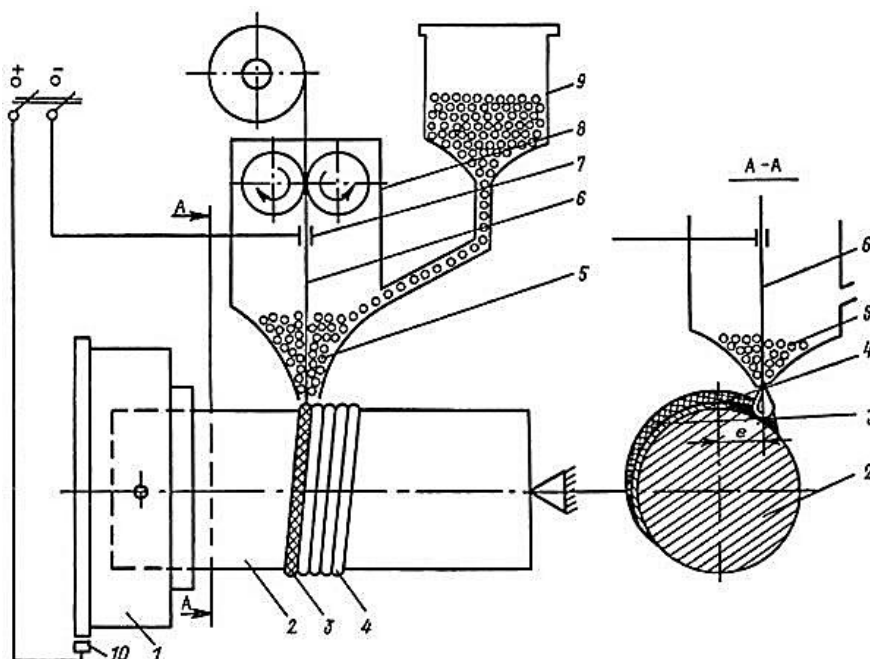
Схема установки наплавки ролика под слоем флюса:
